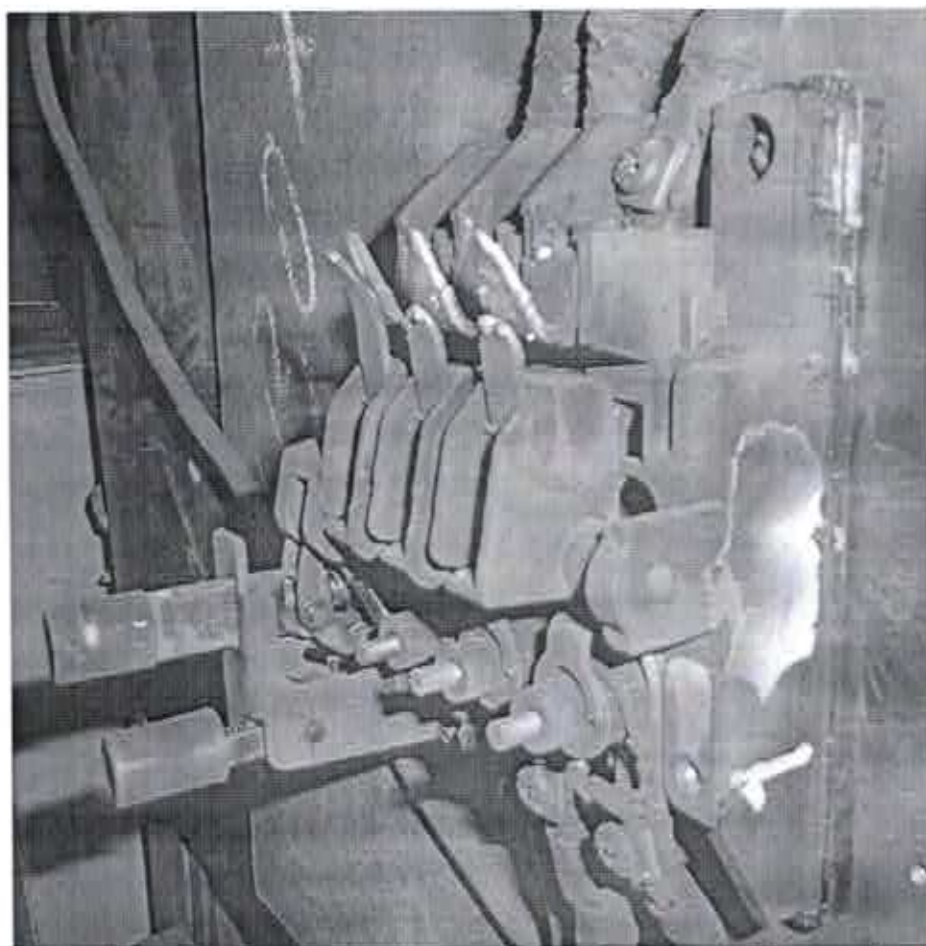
Образец № 1 после испытания на ПКС, вид со снятой крышкой
